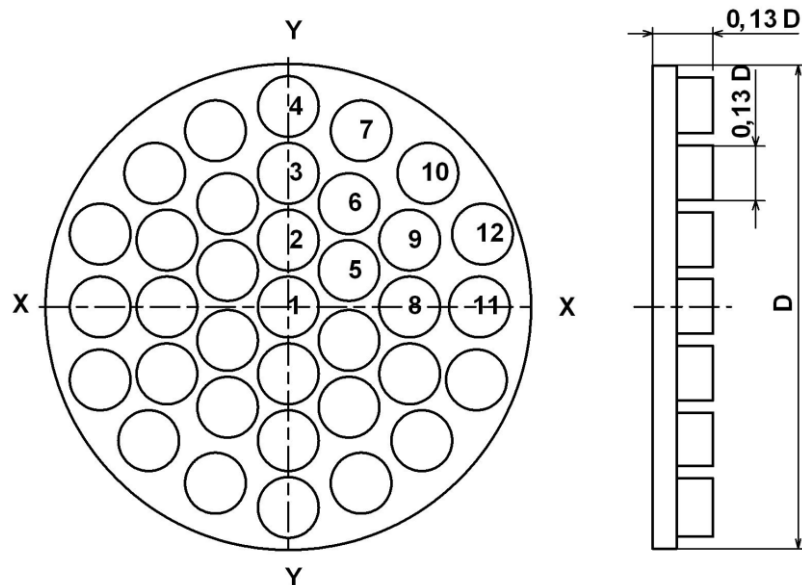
Схема струевыпрямителя потока типа В.
